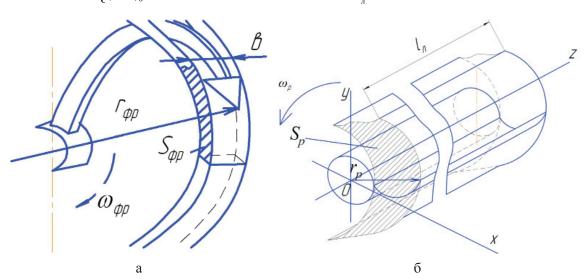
Схема к определению площади боковой проекции стружки питателя: а – фрезерного; б – роторного
